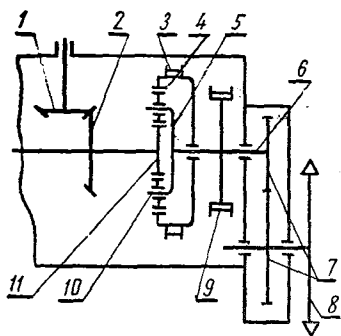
Схема одноступенчатого планетарного механизма поворота:
